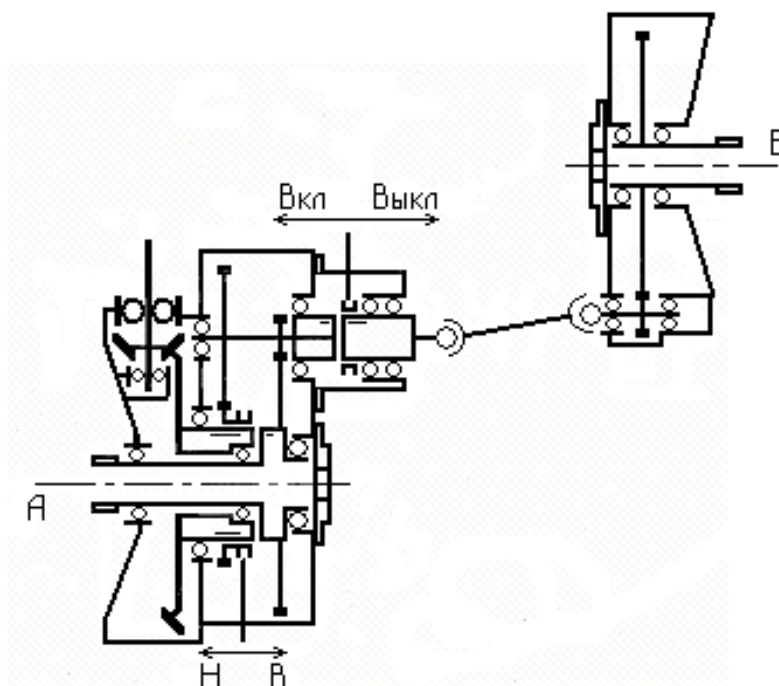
Схема главной передачи с подключаемым приводом колеса бокового прицепа и понижающей передачей. (А- редуктор привода заднего колеса мотоцикла, Б- редуктор
